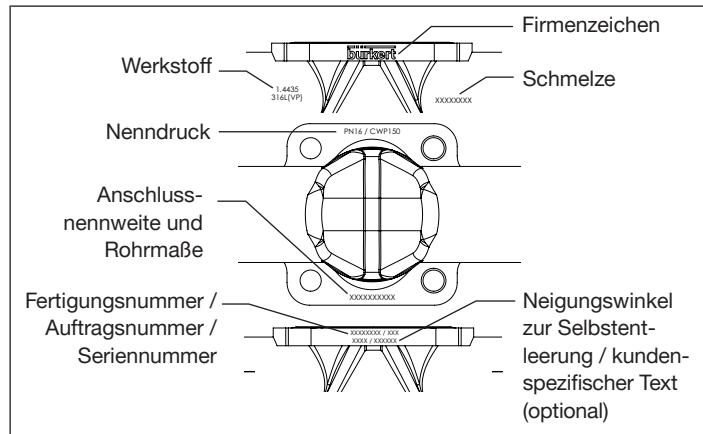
Beschriftung der Rohrumformgehäuse (VP)
